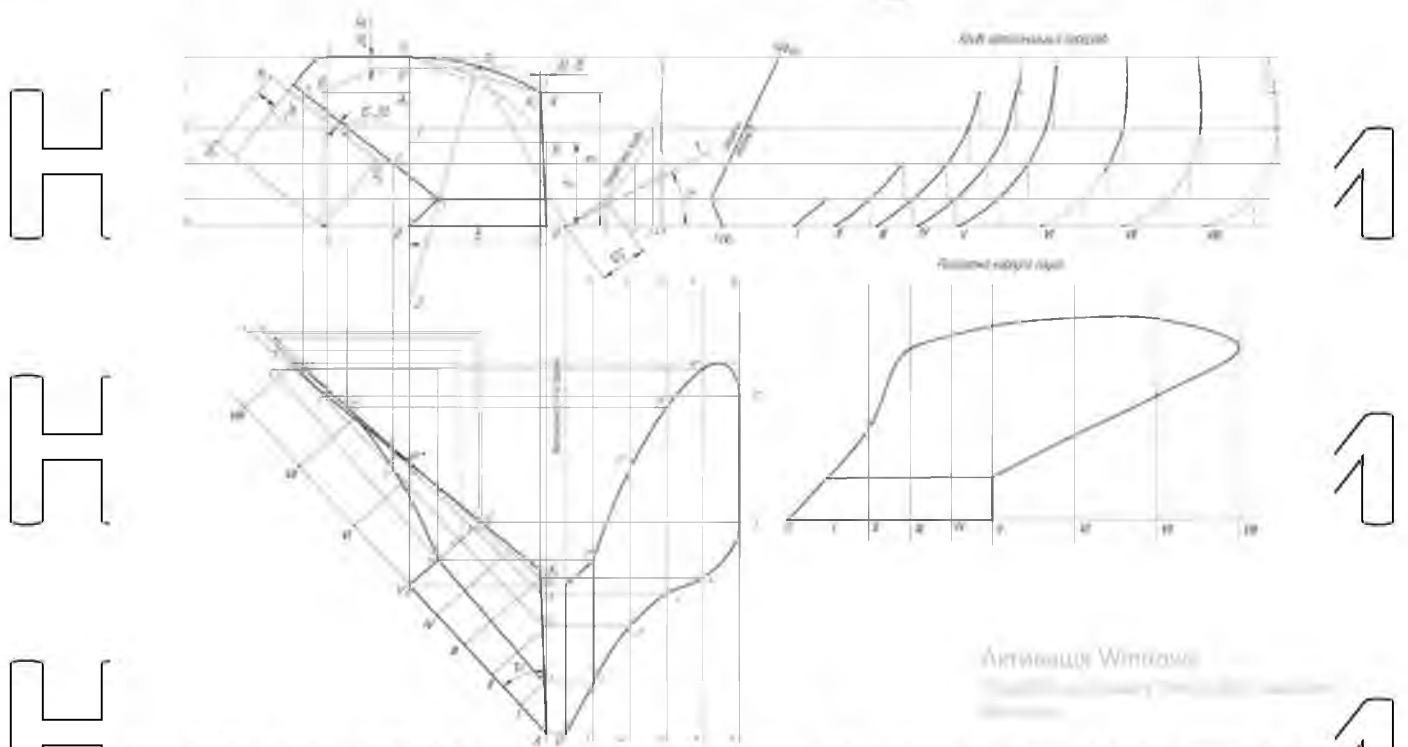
Загальний вигляд спроектованої робочої циліндроїдальної поверхні корпусу плуга
